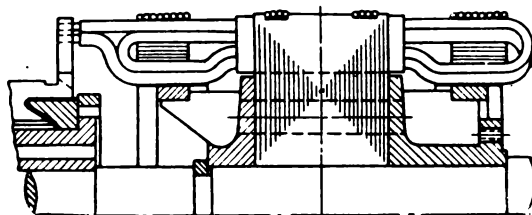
Обмотка якоря из катушек с двойной головкой.
